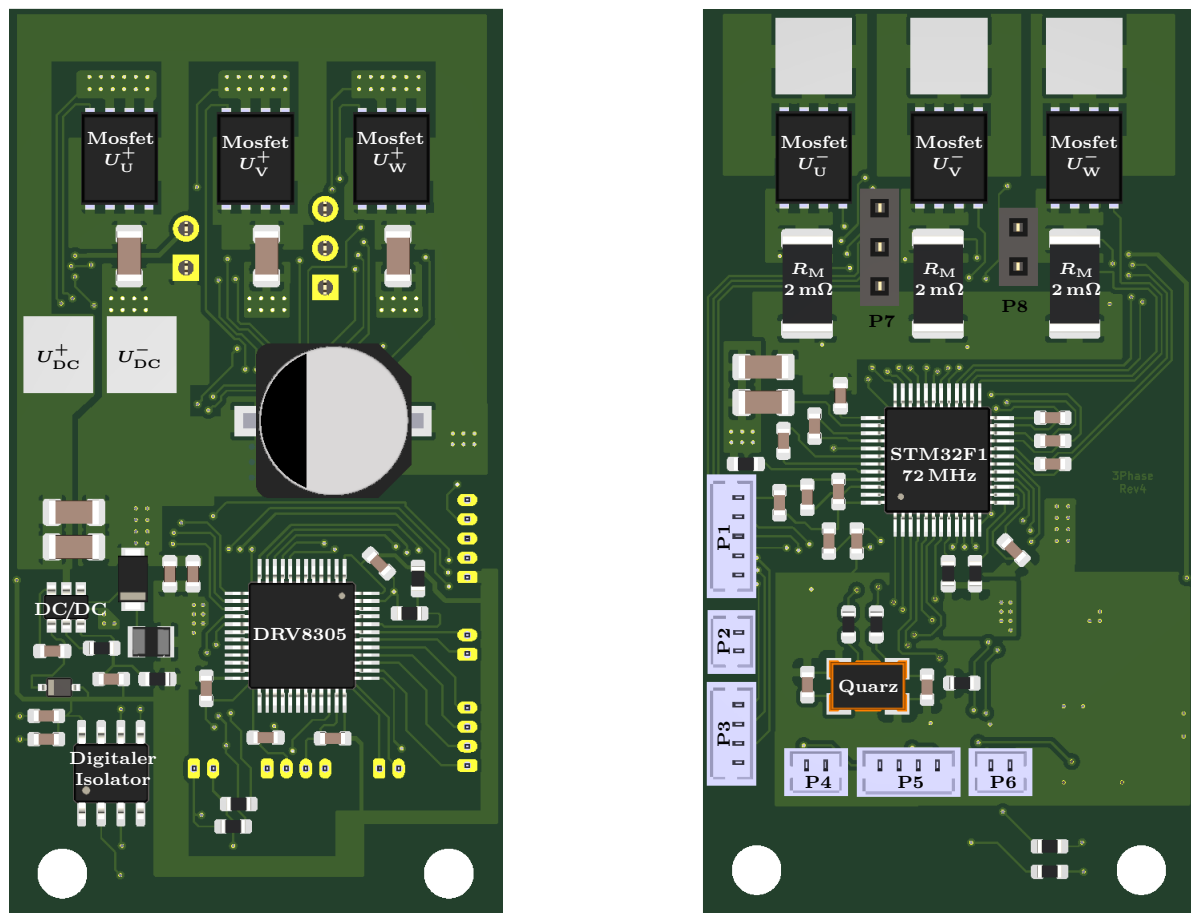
Aufbau des Motorreglers mit Bezeichnung der wichtigsten Bauteile
